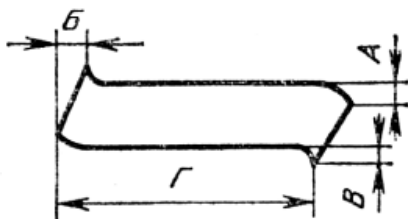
Деформация концов заготовки при отрезке на пресс-ножницах
